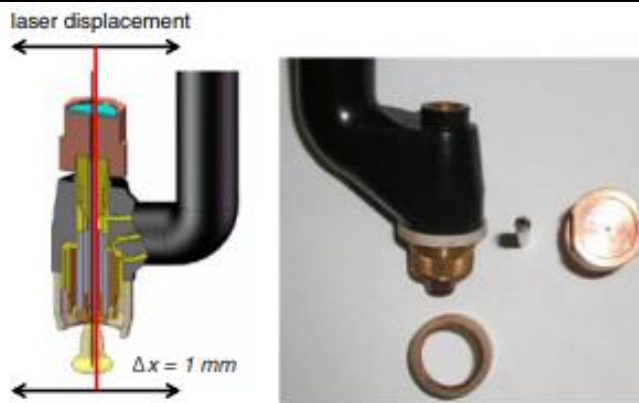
Головка для лазерно-плазменной микросварки и резки металлов малых толщин (мощность излучения 100 Вт, сварочный ток 40 А) [29].
